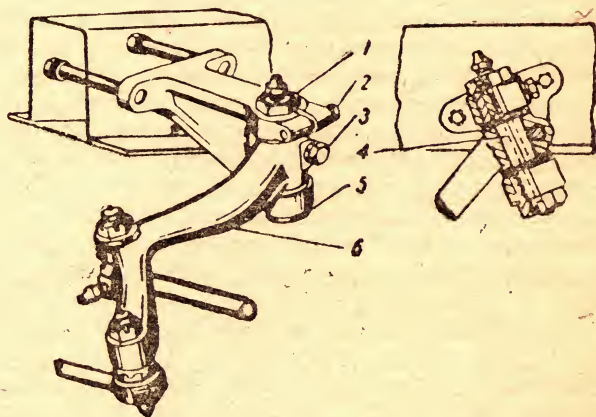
Маятниковый рычаг рулевого привода автомобиля М-21 «Волга»
